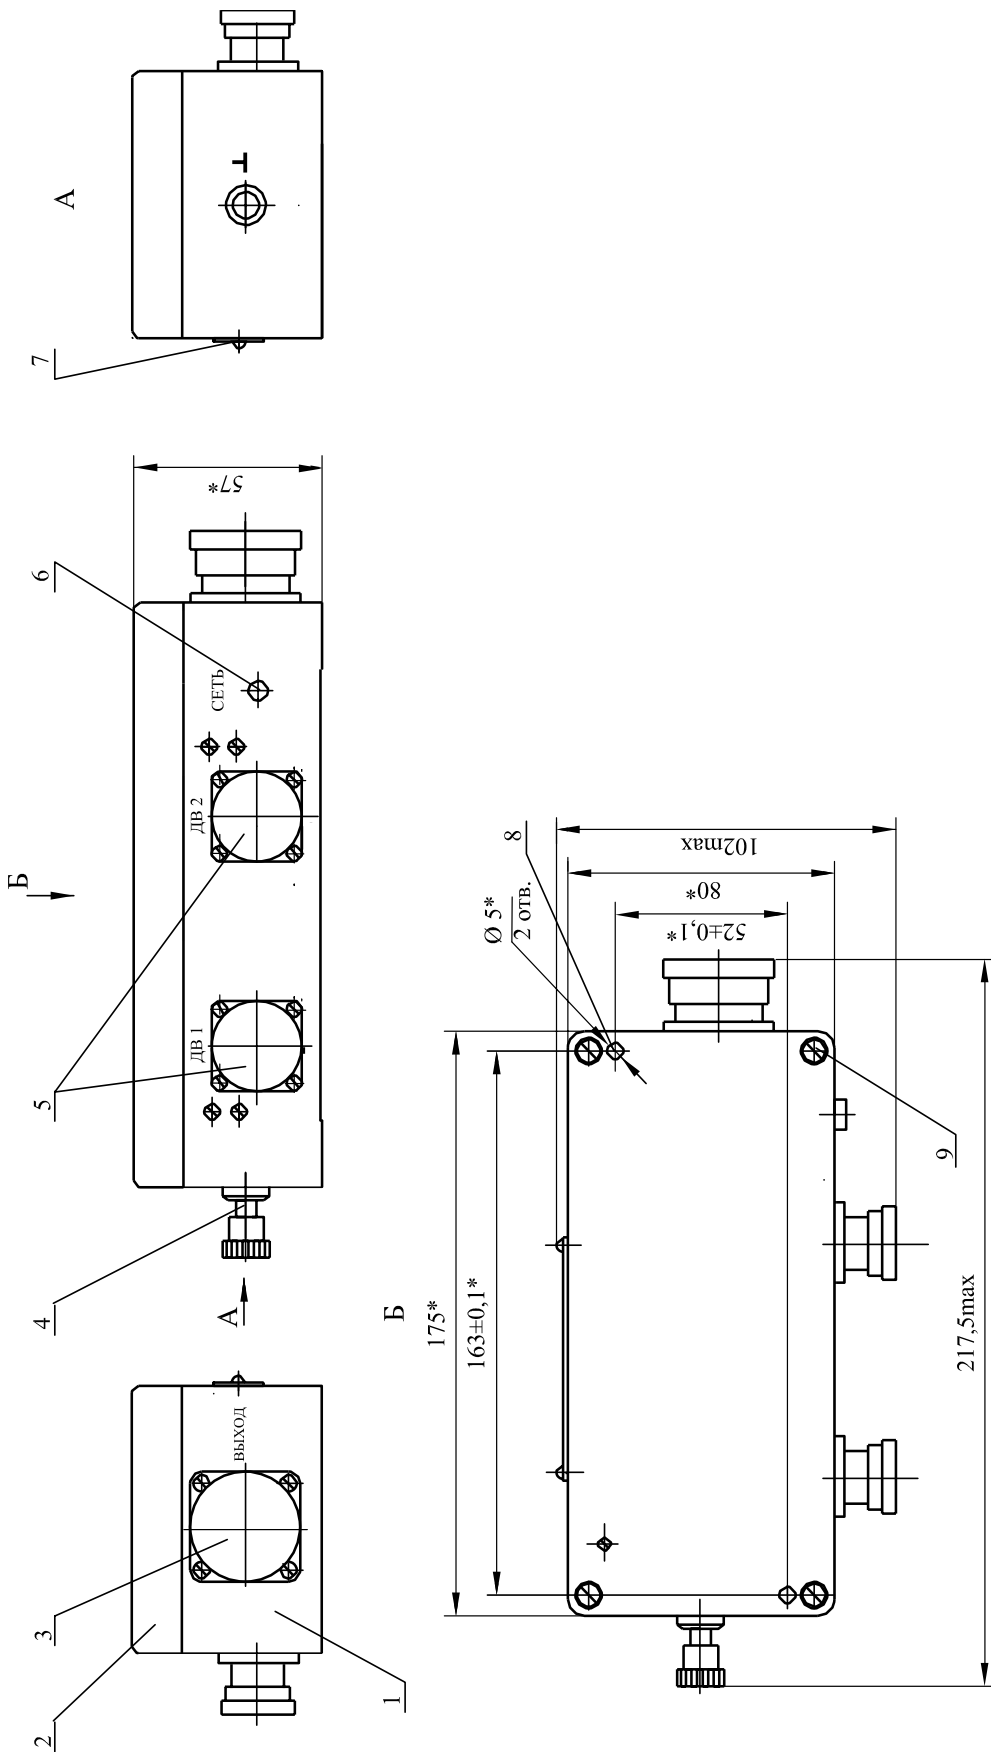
(1 из 2) - Габаритно - установочные размеры согласующего блока БС-16-48
